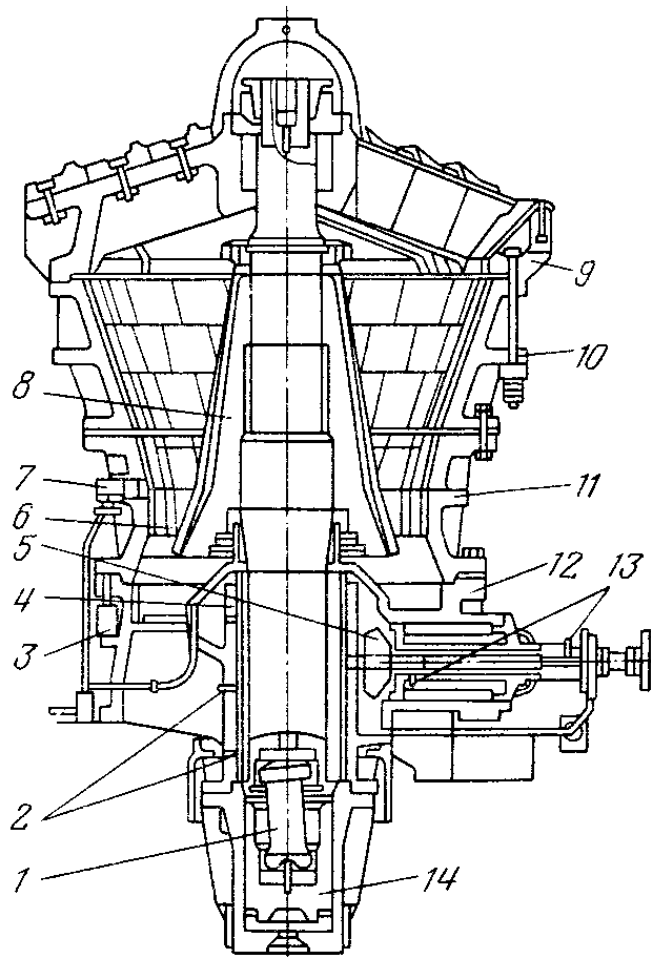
Принципова схема конусної дробарки крупного дроблення:
